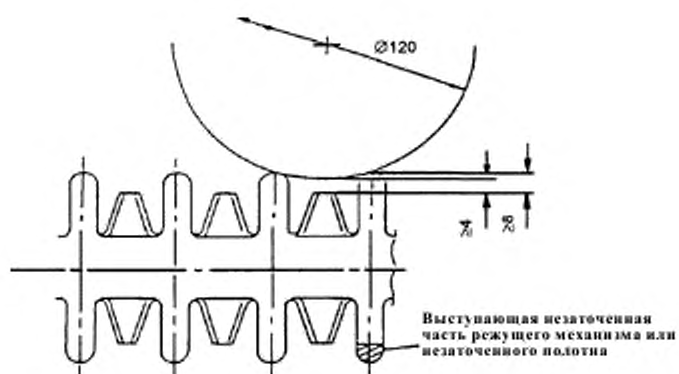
Исполнения режущего механизма для категорий 1 и 2 (см. таблицу 101)
